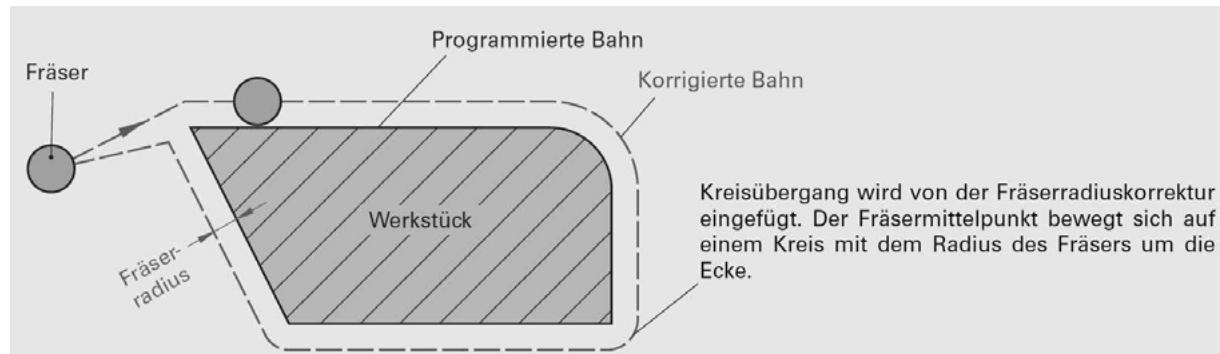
Prinzip der Fräserradiuskorrektur⁹⁶¹
